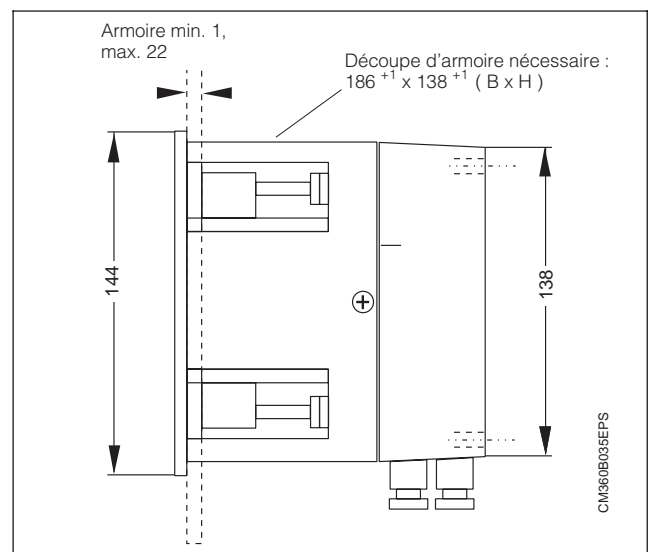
PoolPac, vue latérale avec découpe d'armoire
